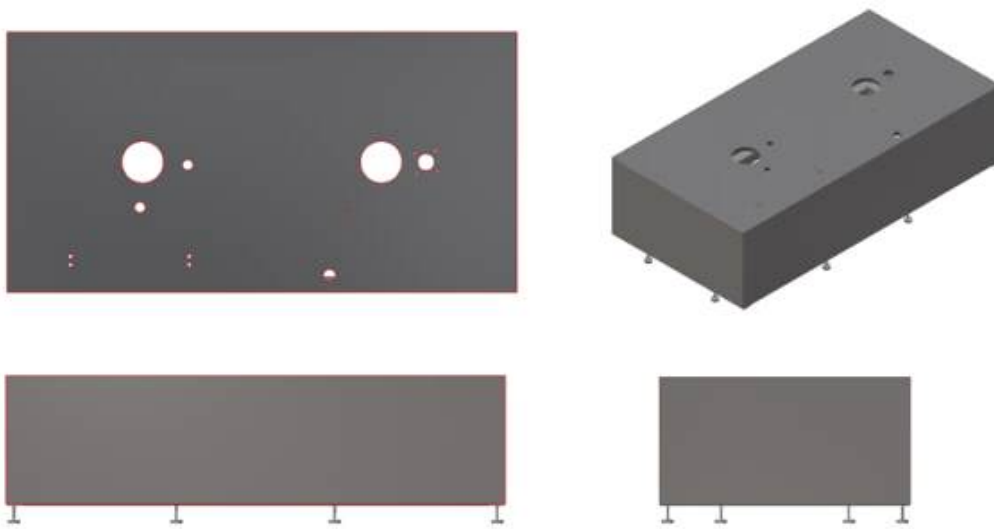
Auto Packaging Machine Main Frame 3D 모델링 형상
